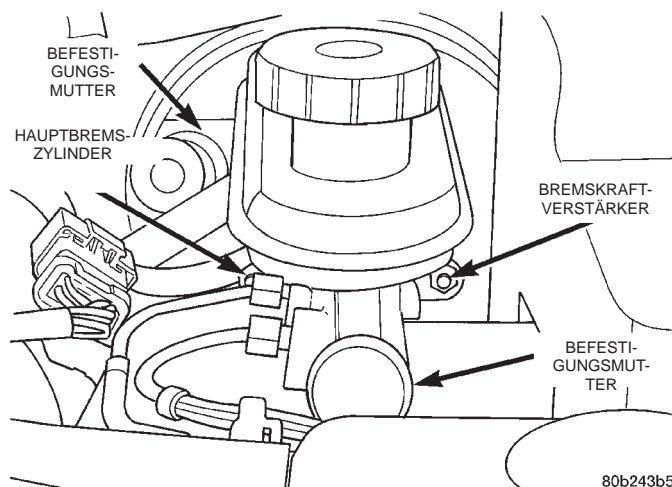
Befestigung/Hauptbremszylinder an Bremskraftverstärker
